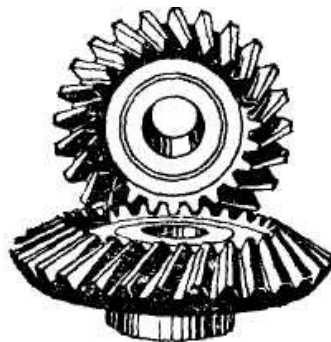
Колеса с косыми или тангенциальными зубьями
